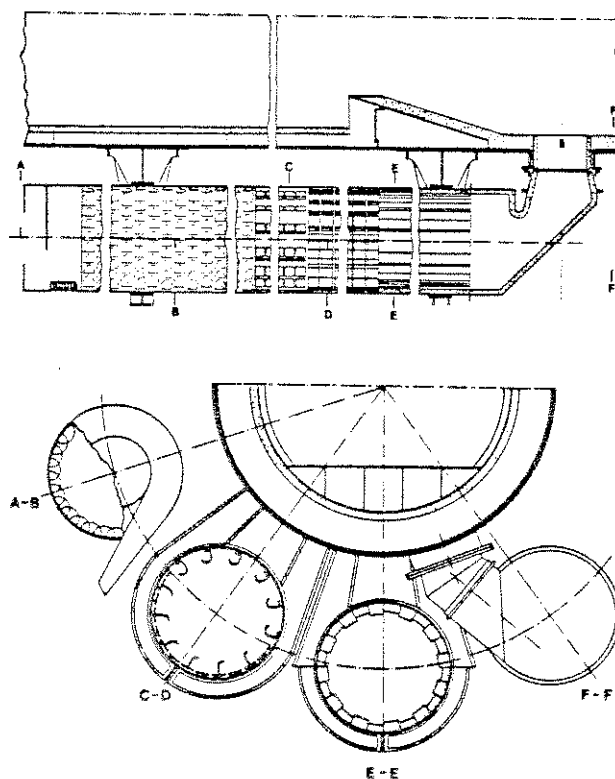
Längsschnitt durch den neuen Unax-Kühler mit dazugehörigen Querschnitten
